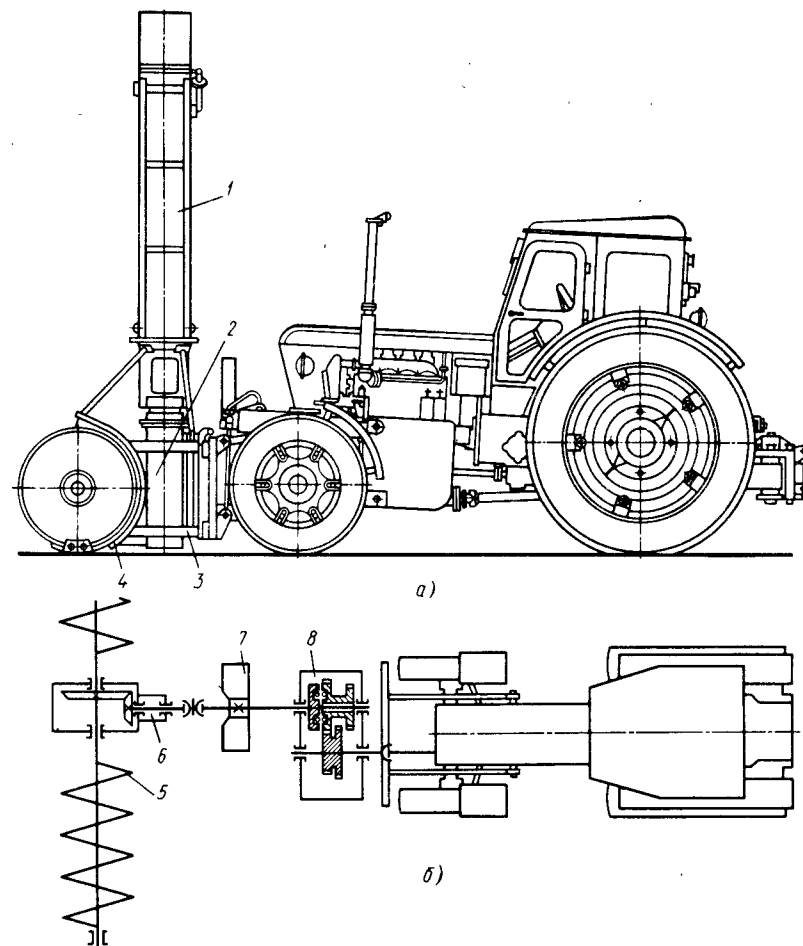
Универсальная уборочная машина КО-705 с фрезерно-роторным оборудованием:
